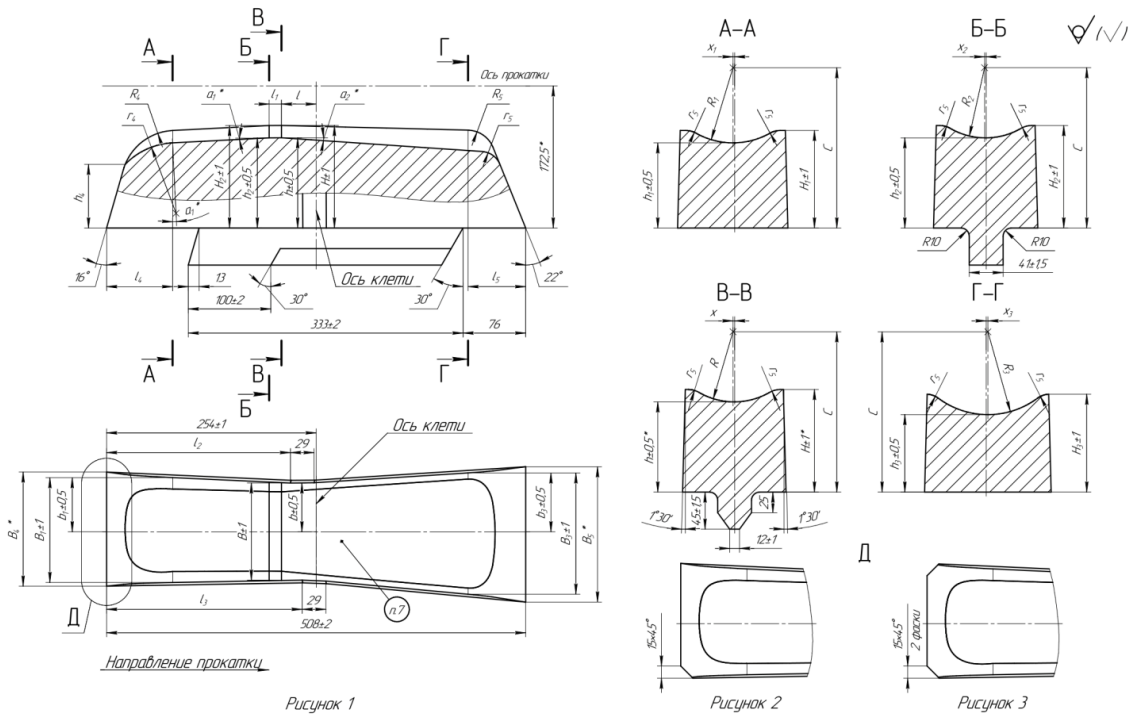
Новая калибровка линейки для удлиненной бочки ТПА 220
